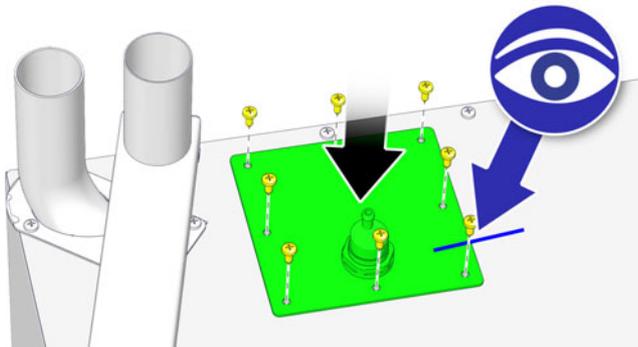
Tôle de montage du capteur de niveau de remplissage
